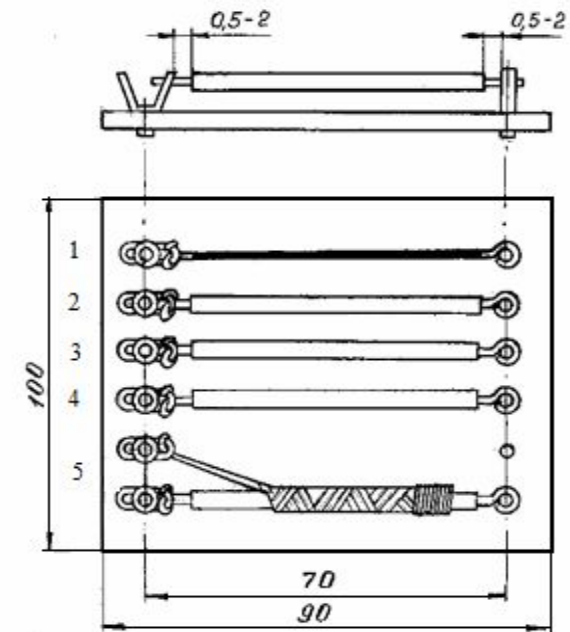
Расположение монтажных проводов на типовой плате:
